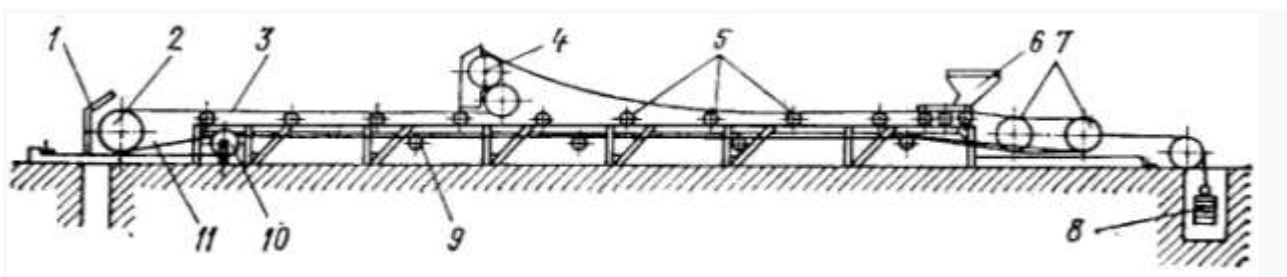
Стрічковий конвеєр: 1 - розвантажувальна воронка; 2 - приводний барабан; 3 - робоча гілка стрічки; 4 - пересувний скидаючий пристрій; 5 - роликоопори робочої гілки стрічки; 6 - завантажувальна воронка; 7 - натяжний барабан; 8 - вантаж натяжного пристрою ; 9 - роликоопори холостої гілки стрічки; 10 - відхиляючий барабан; 11 - холоста вітка стрічки
